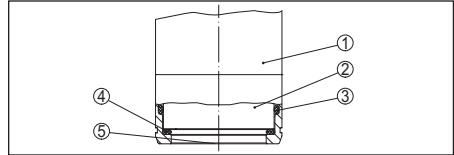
Montaje frontal rasante de la celda de medida CERTEC® con junta doble
